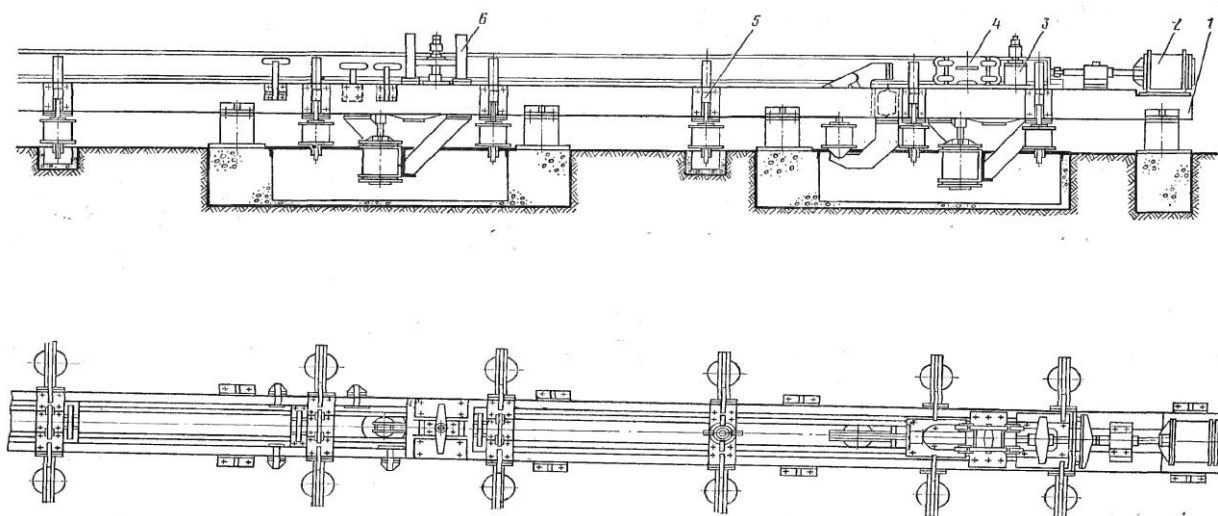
Кондуктор для сборки и сварки хребтовой балки рамы пассажирского вагона [15]
